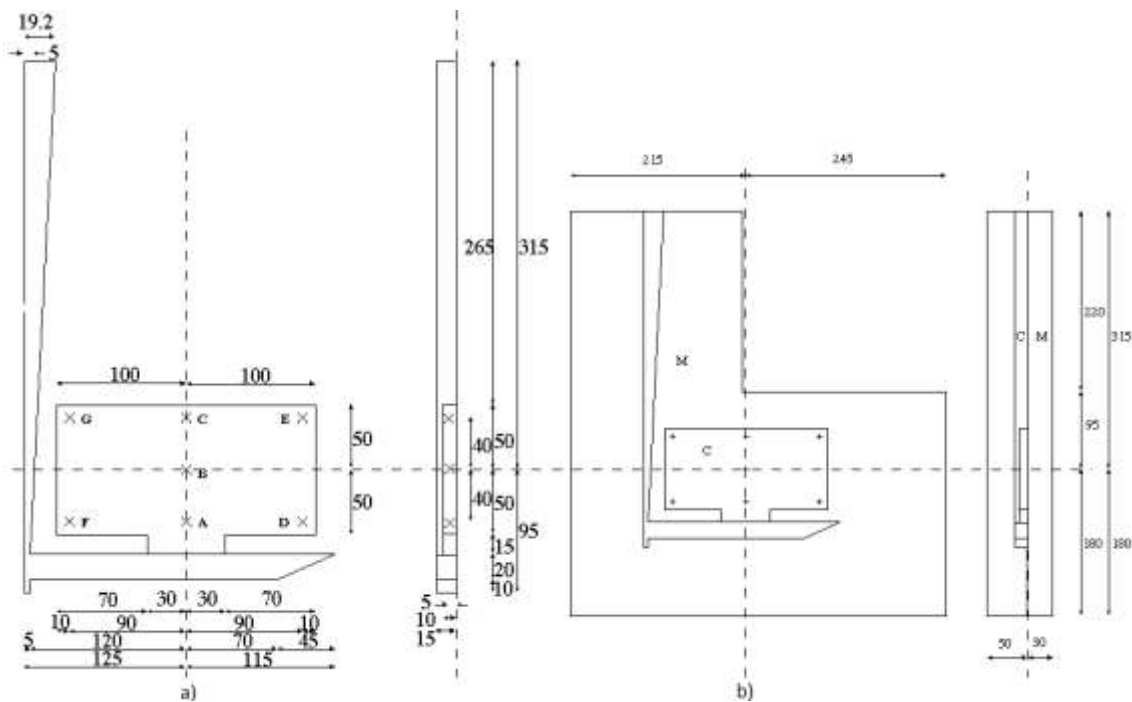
Dimensiones del modelo, a) dimensiones internas del molde y b) dimensiones de la caja de molde (cantidad de arena) y vista izquierda, todas las dimensiones [mm], las cruces son termopares (Campbell, 1995).
